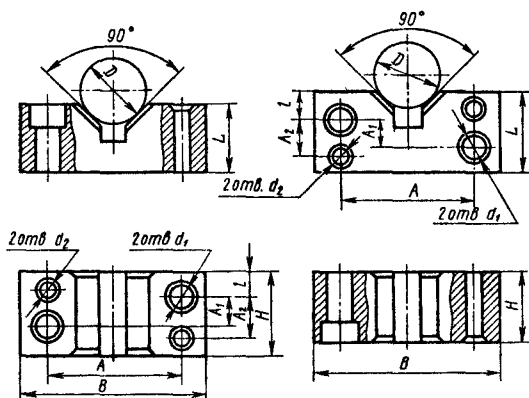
Схемы базирования заготовок наружной цилиндрической поверхностью:
